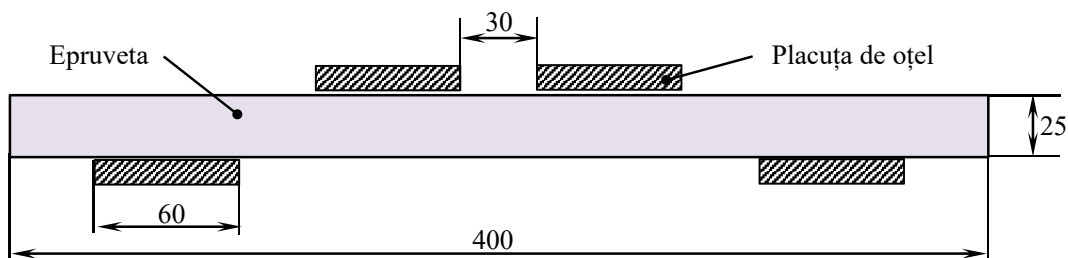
Dimensiunile epruvetei, în mm
